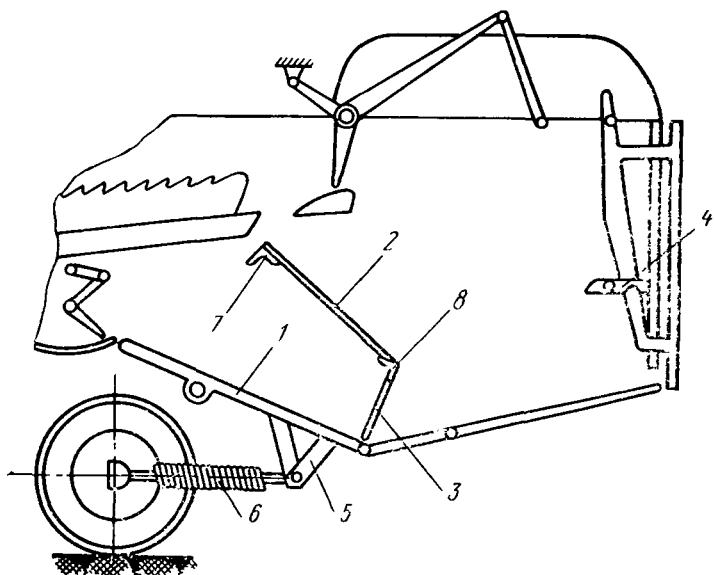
Схема приспособления к копнителю для сбора половы:
